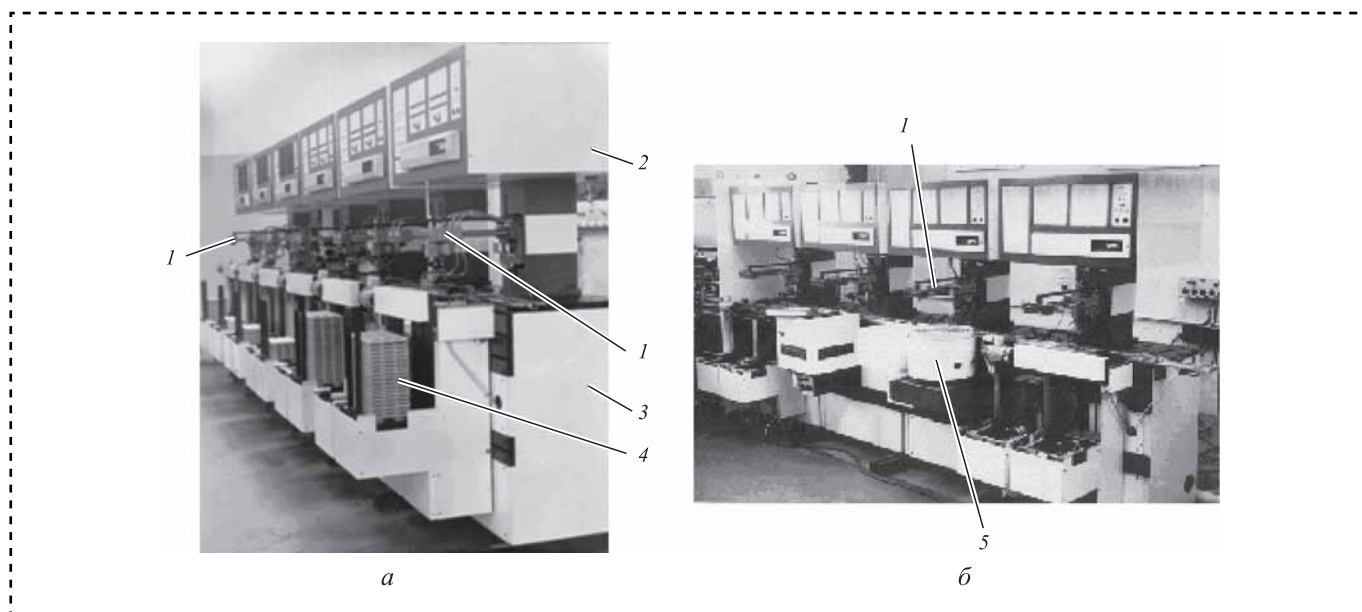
Линия модульного типа для сборки металлокерамических корпусов ИМС с планарными выводами:
